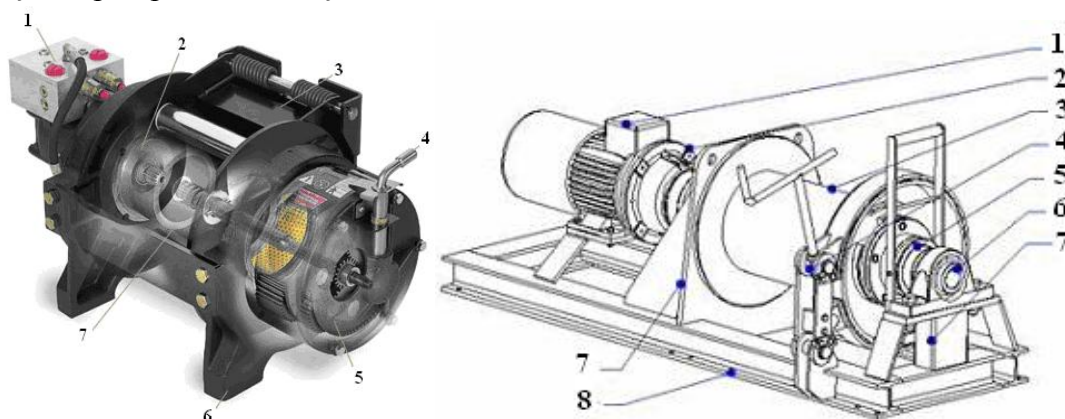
Vinci hidraulic: 1- motor hidraulic; 2- redactor de turație; 3- tambur cilindric; 4- frână cu bandă; 5- ambreiaj; 6- lagăr de capăt; 7- suportul tamburului; 8- cadru de bază.
